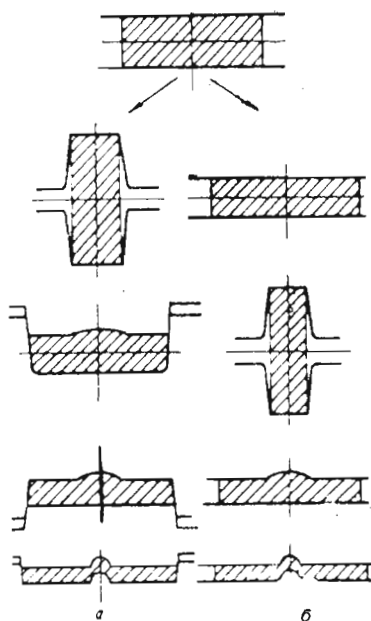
Возможные схемы калибровки и прокатки желобчатой рессоры:
